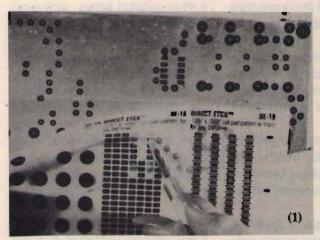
Applicazione diretta sul rame delle piazzole trasferibili.
